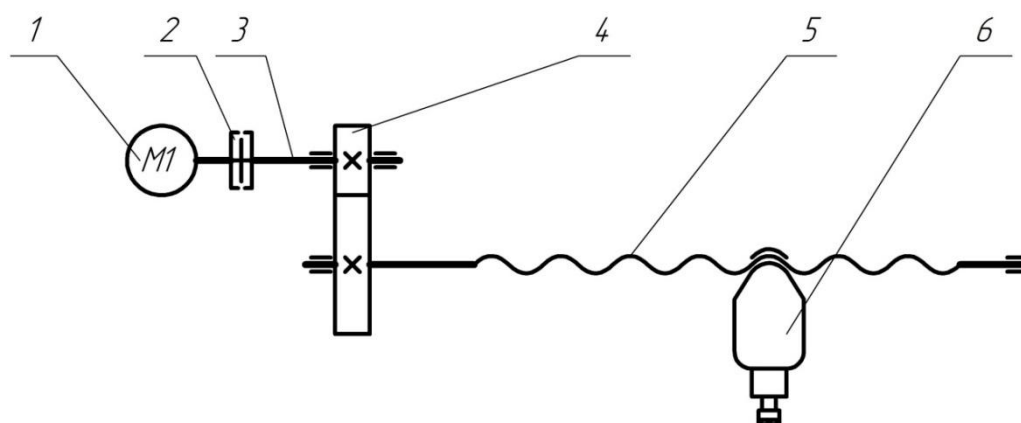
Привод фрезерної голівки: 1 – Електродвигун; 2 – дискова двостороння муфта зчеплення; 3 – вал; 4 – редуктор; 5 – Нерозмірна передача «гвинт-гайка»; 6 – силова фрезерна голівка.
